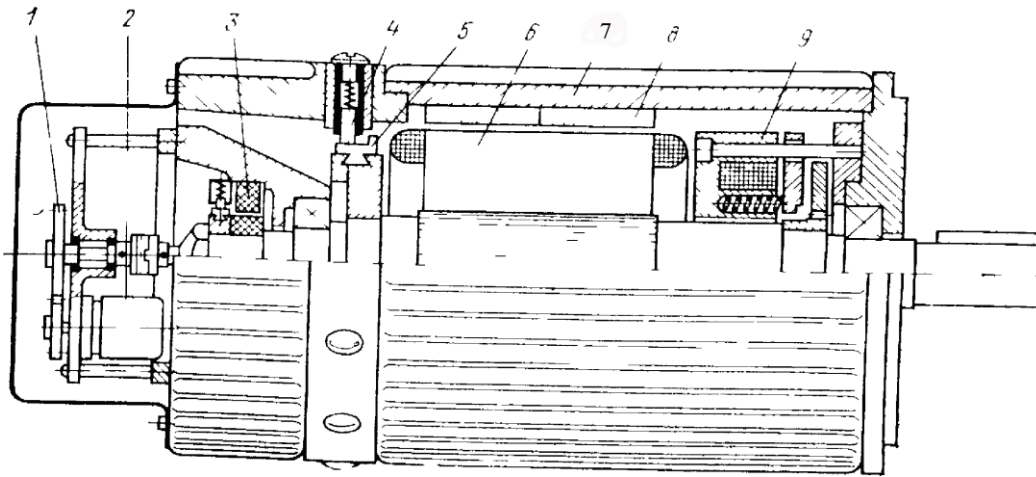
Конструктивная схема высокомоментного двигателя: 1 — повышающая передача (мультипликатор); 2 — резольвер; 3 — тахогенератор; 4, 5 — коллекторы; 6 - ротор; 7 — корпус статора; 8 — ферритовые полюсы; 9 — электромагнитный тормоз
